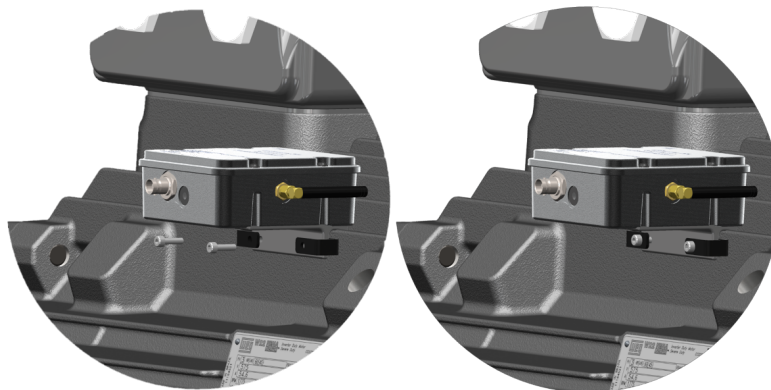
Montagem do conjunto de sensor com presilha para aleta do motor.
